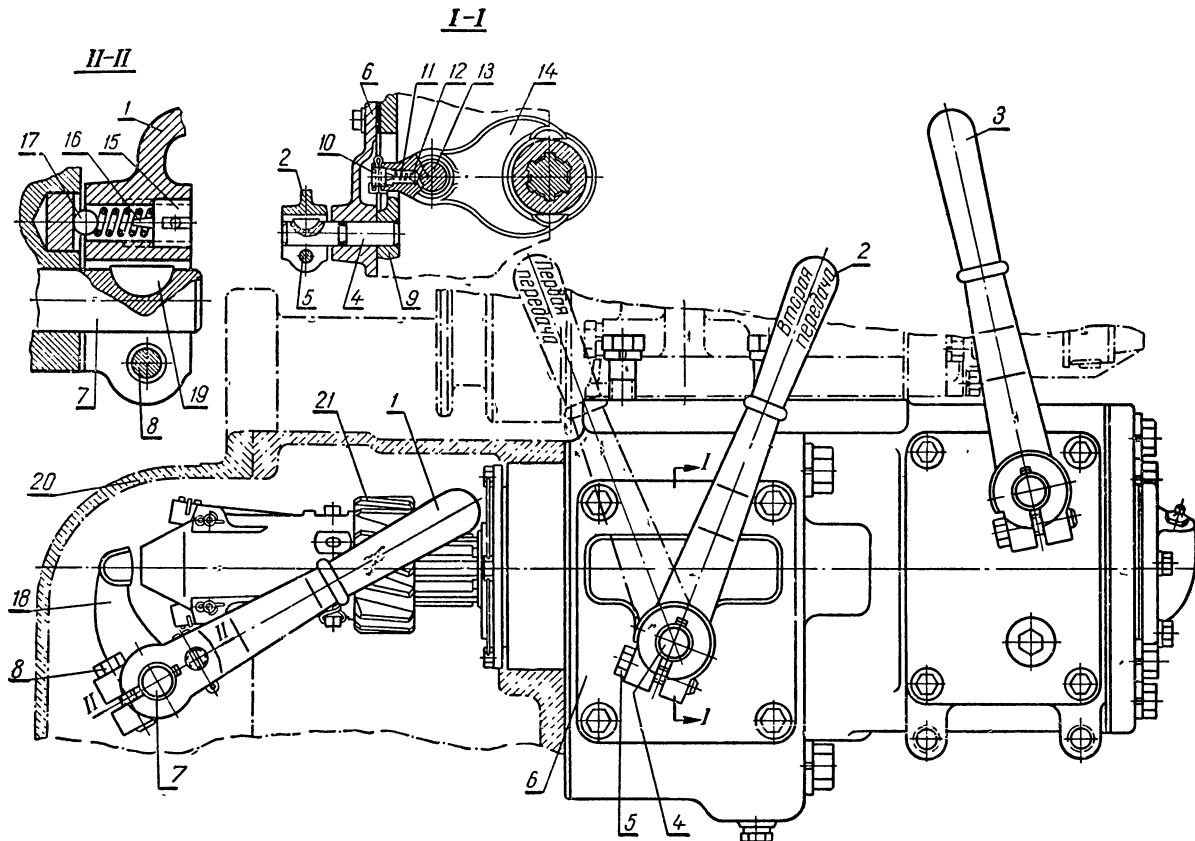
Рычаги управления механизмами силовой передачи пускового устройства:
